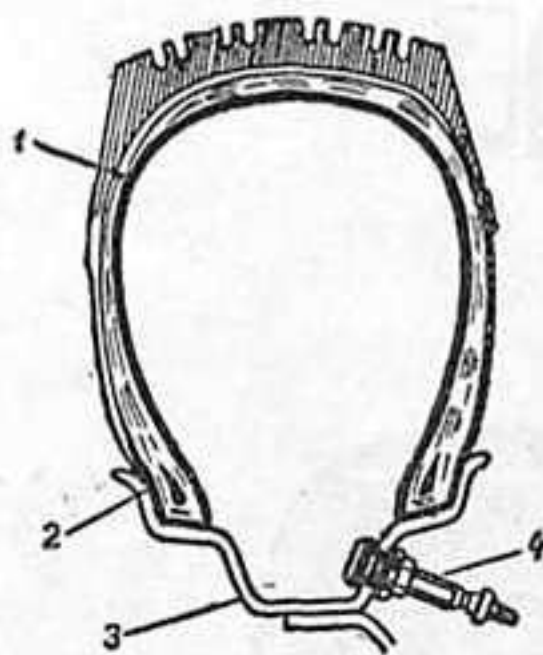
Бескамерная шина на ободе (разрез). 1 — Внутренний герметизирующий слой. 2 — Бортовой уплотнительный слой. 3 — Обод. 4 — Вентиль с резиновыми шайбами.
